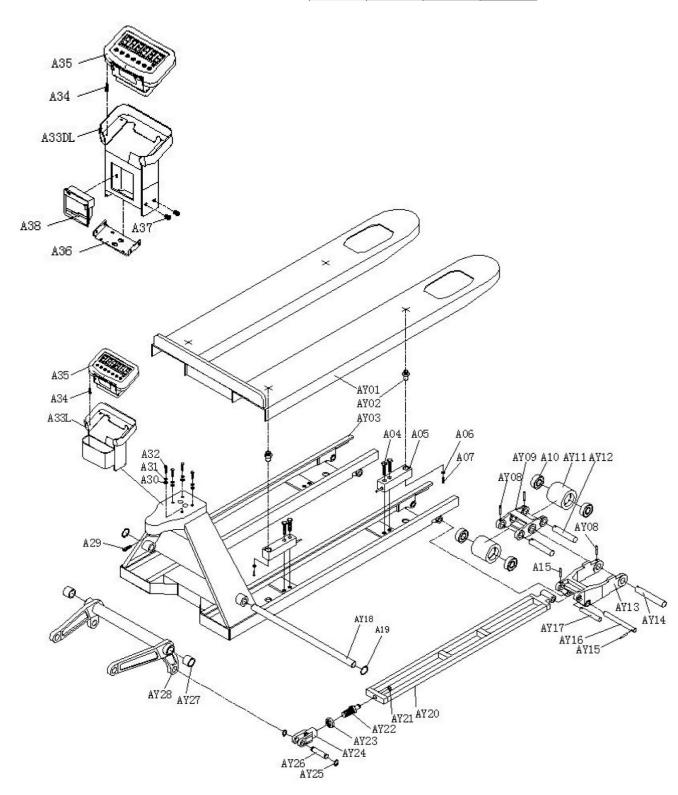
Взрыв-схема корпуса тележки WH-ES.
